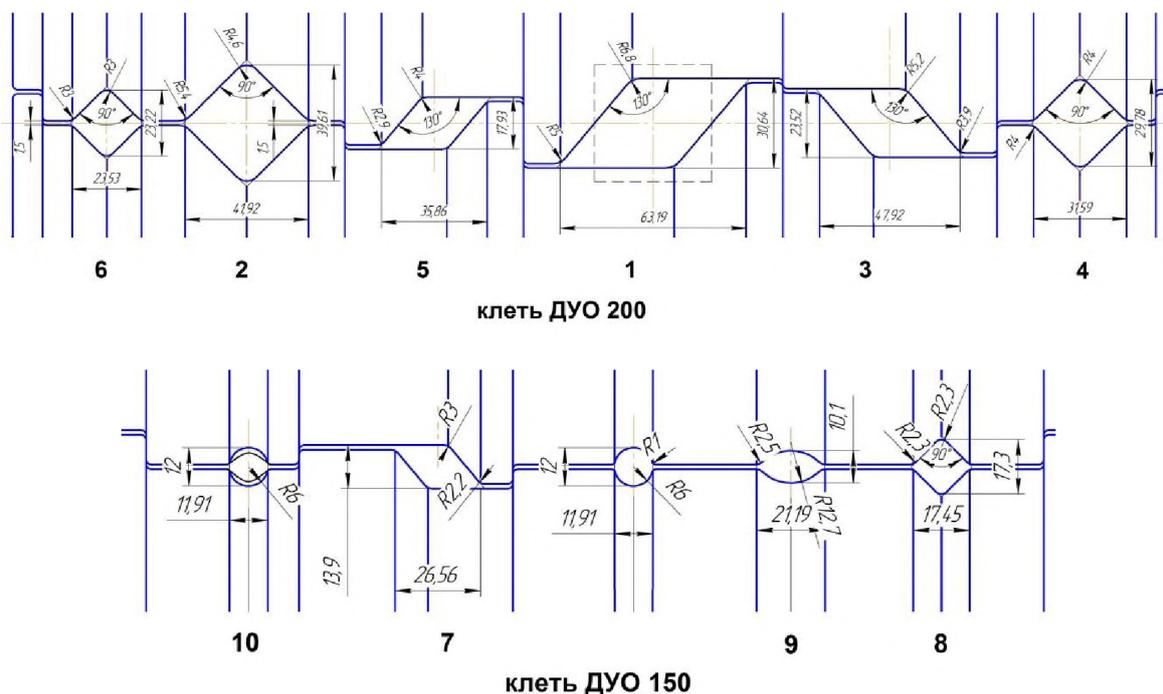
Эскиз калибровок рабочих валков стана «ДУО 200/150»
